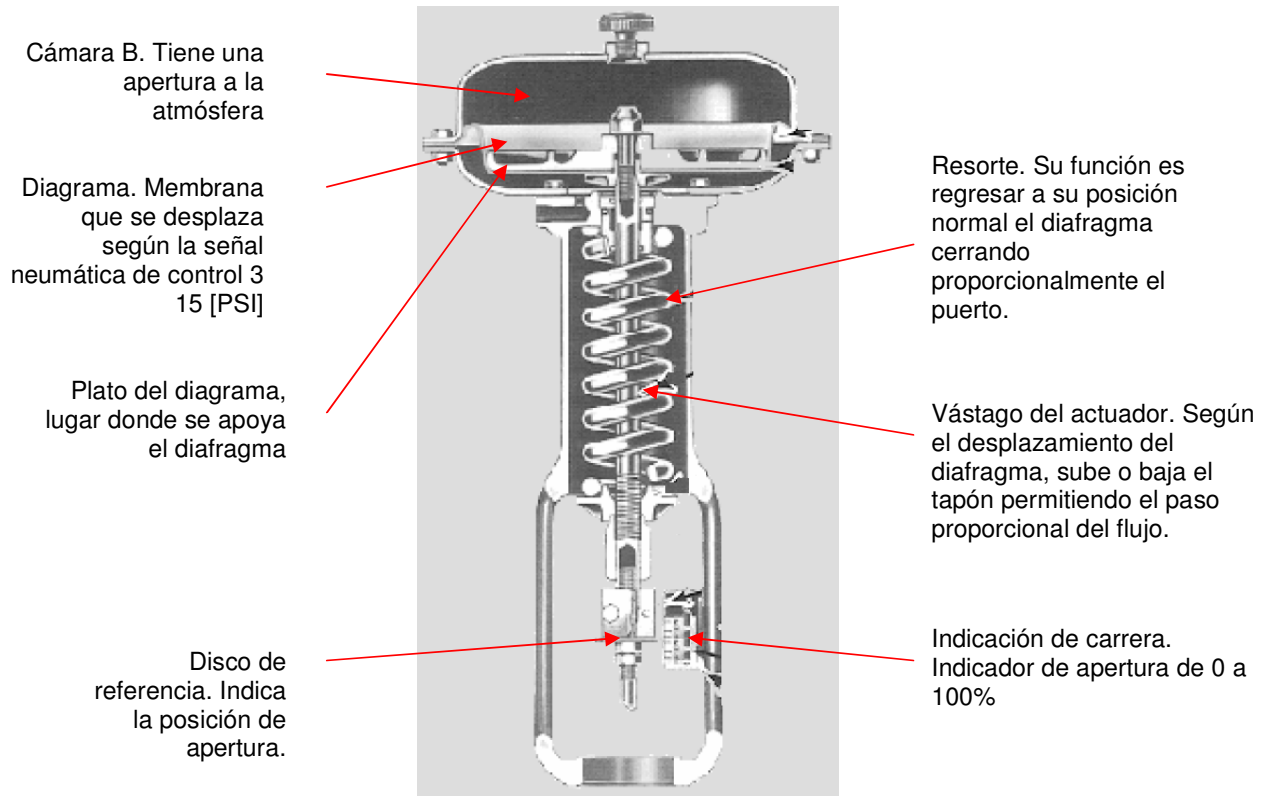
PARTES INTERNAS DEL ACTUADOR NEUMÁTICO
